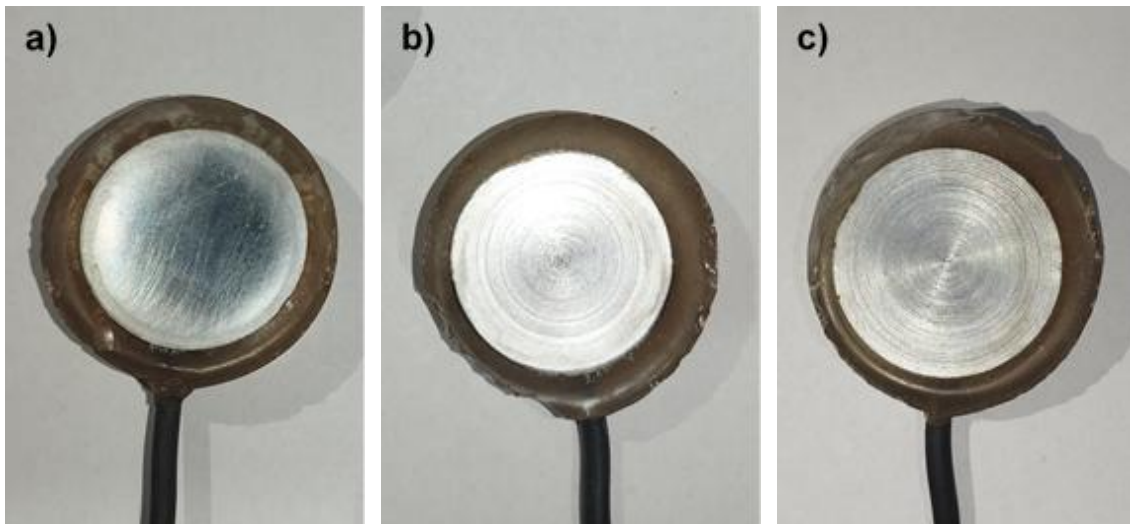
Surfaces planes chromées : a) polie ; b) brunie ; c) usinée
